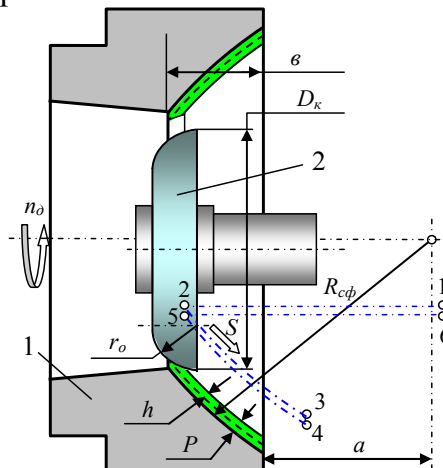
Схема шлифования сферической поверхности на круглошлифовальном станке с ЧПУ
